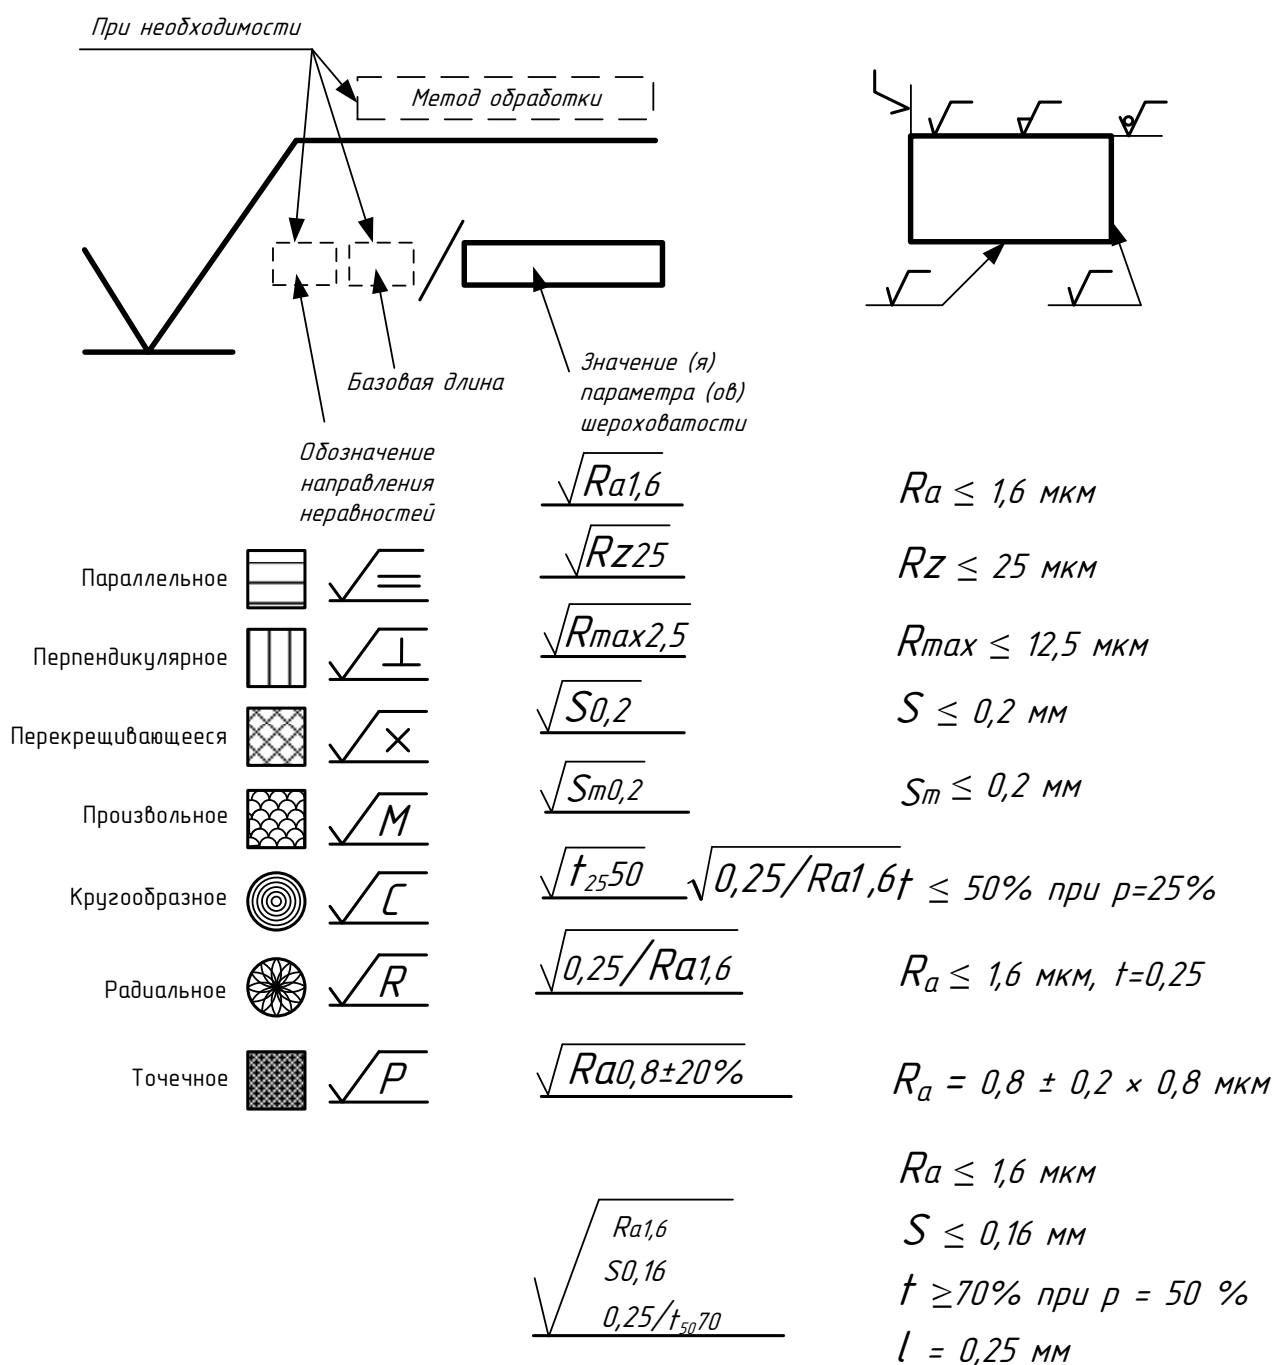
Структура и примеры обозначения шероховатости
